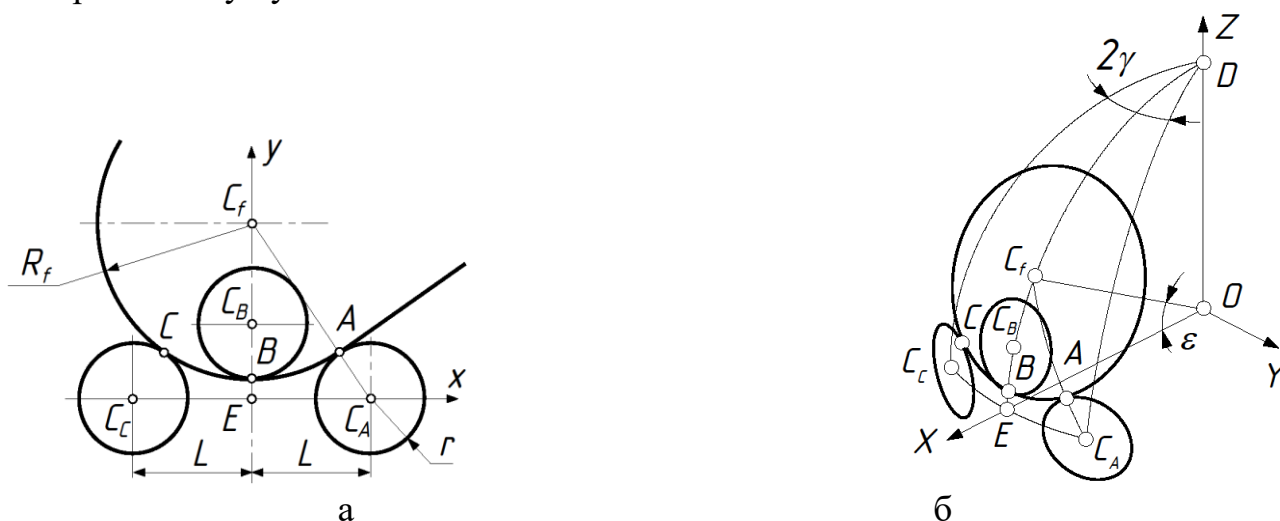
Розрахункові схеми для налаштування валків для прокатки:
